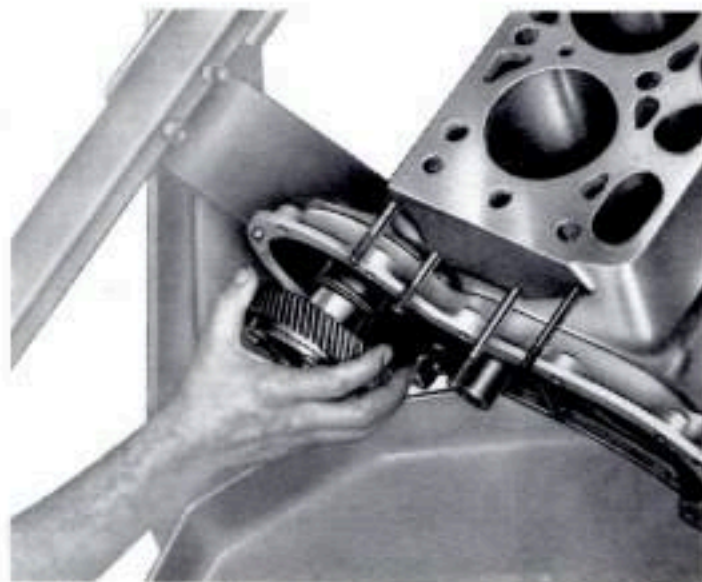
Smontaggio del motore: viene asportato l'ingranaggio comando pompa iniezione.
